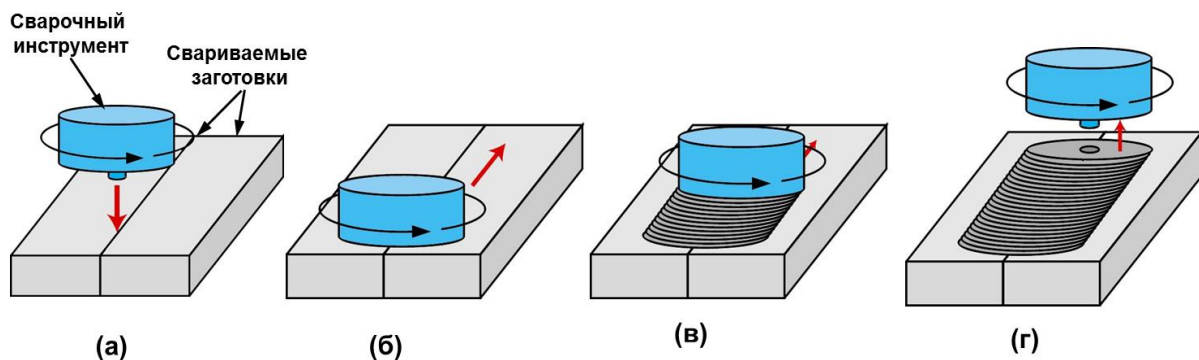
Принципиальная схема обработки трением с перемешиванием: (а) вращение сварочного инструмента, (б) его введение в стык между двумя свариваемыми заготовками, (в) перемещение вращающегося инструмента вдоль стыка и (г) извлечение инструмента из сварного шва по окончании процесса обработки.
